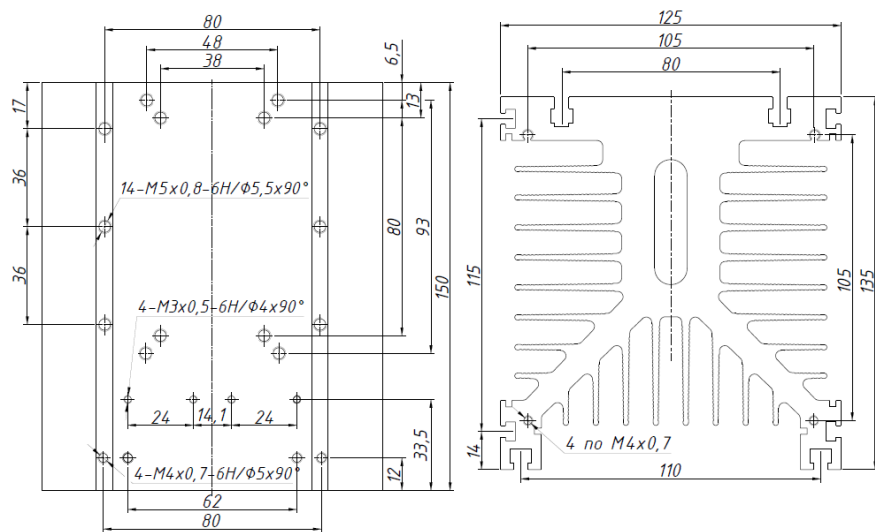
габаритные и установочные размеры радиатора PTP038
